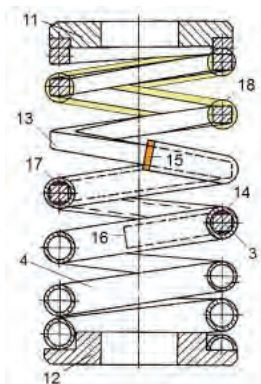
Фронтальный разрез цилиндрической вибродемпфирующей пружины
